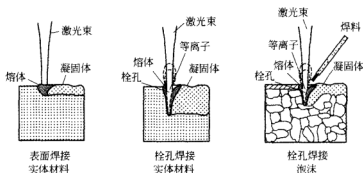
激光束焊接中的表面焊接和栓孔焊接
